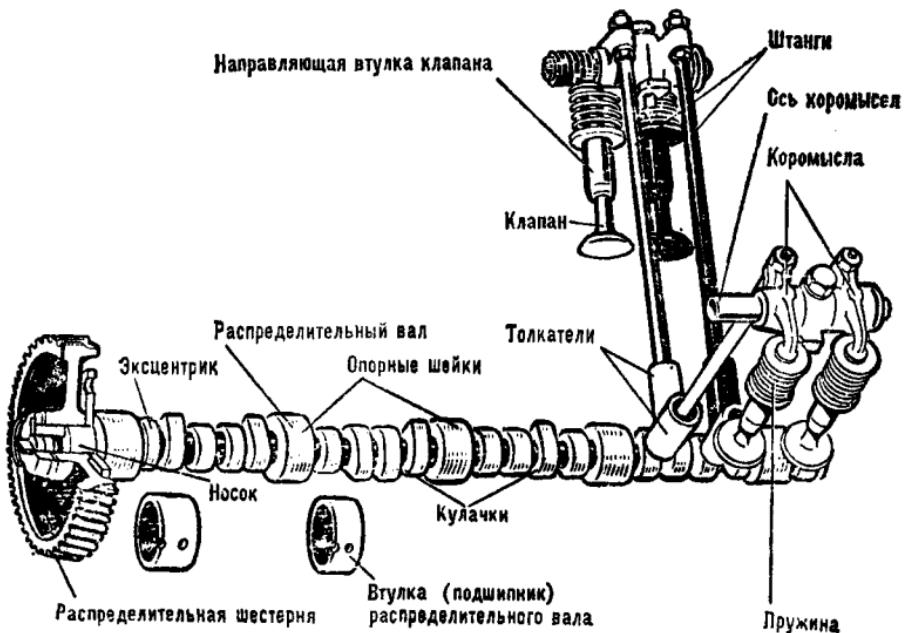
Газораспределительный механизм с верхним расположением клапанов
